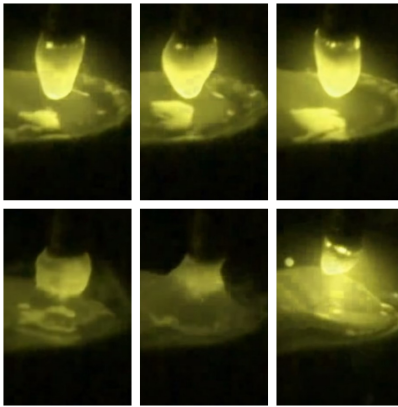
ARCO CORTO CIRCUITO SOLDADURA MIG/MAG EN CÁMARA LENTA.
